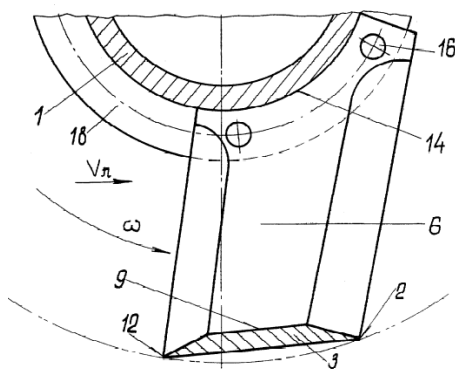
Общий вид рабочего органа почвофрезы по патенту РФ № 2294072
